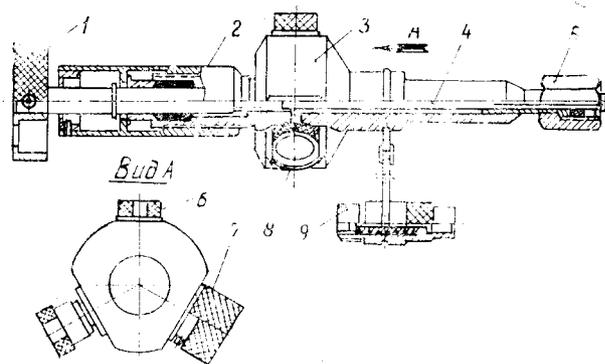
Приспособление № 63740/028 для проверки давления в стойках шасси и шинах:
